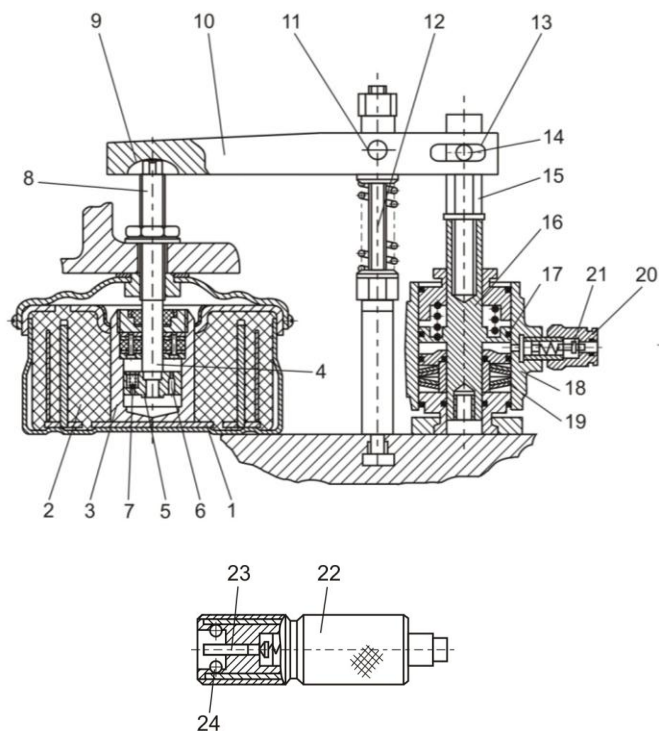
Общий вид виброизолирующего устройства: 1 – основание; 2 – резиновый элемент; 3 – цилиндр; 4 – шток; 5 – поршень; 6 – калиброванное отверстие; 7 – клапан сжатия; 8 – регулировочный винт; 9 – сферическая поверхность лунки; 10 – прихват; 11 – ось; 12 – стойка; 13 – продольный паз; 14 – ось; 15 – опора; 16 – опорный шток; 17 – поршень; 18 – гидроцилиндр; 19 – пружинный аккумулятор; 20 – малая полумуфта; 21 – клапан; 22 – большая полумуфта; 23 – клапанный штырь; 24 – шарики
